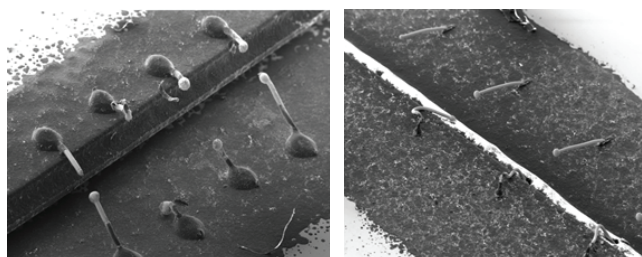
вид перемычек после испытания на допустимую токовую нагрузку. Слева распаянные перемычки, справа – перемычки, созданные термозвуковой сваркой
